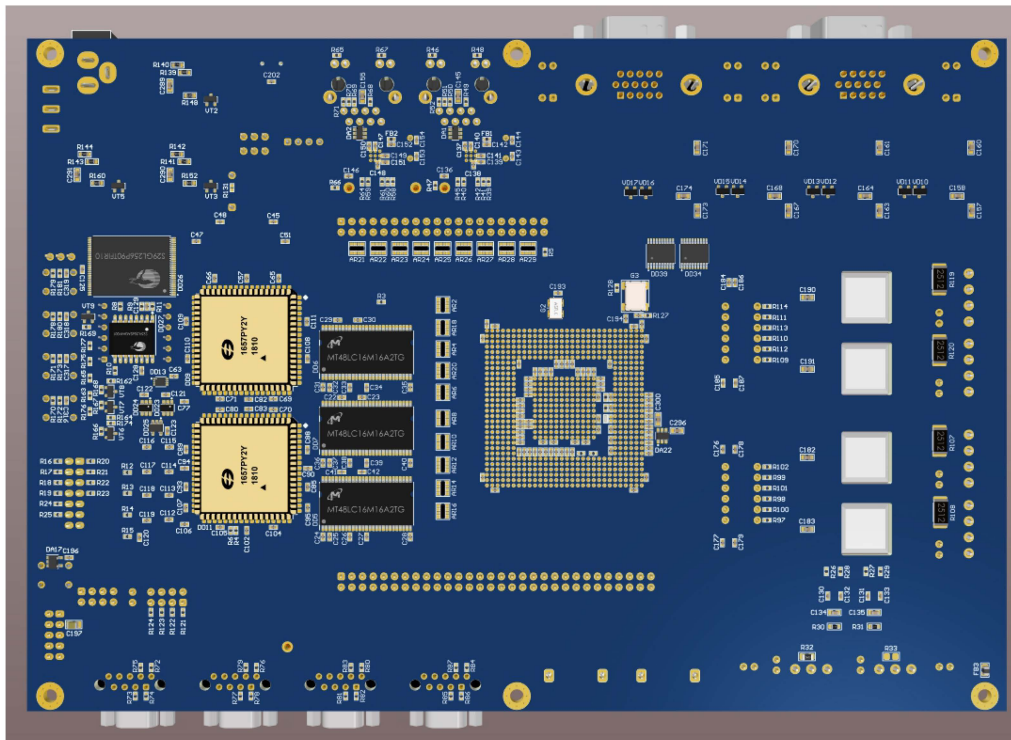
Внешний вид отладочного модуля. Обратная сторона
